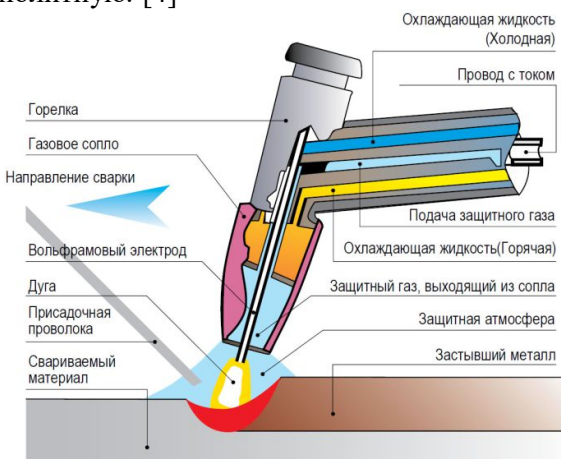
Наплавка с подачей жидкого металла расплавляемой присадочной проволоки в сварочную ванну. Зона наплавки защищена защитным газом.
